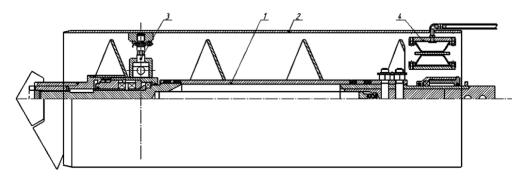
Устройство корректировки траектории: 1 – вал; 2 – корпус трубы; 3 – передняя подвеска; 4 – задняя подвеска
